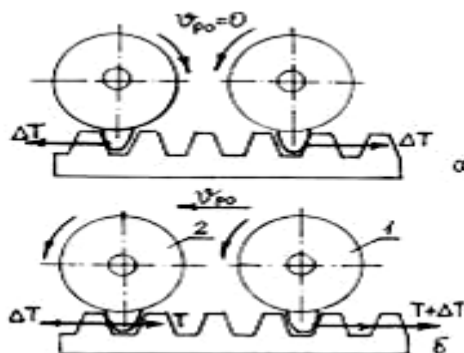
Схемы выбора зазоров установкой двух червяков
